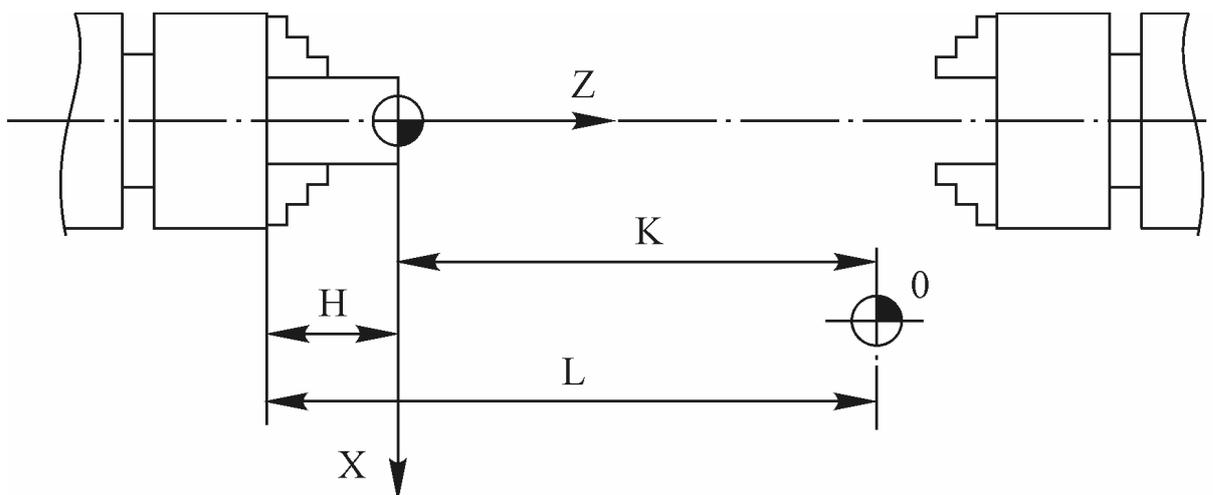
Схема привязки режущего инструмента к нулю детали по оси Z
